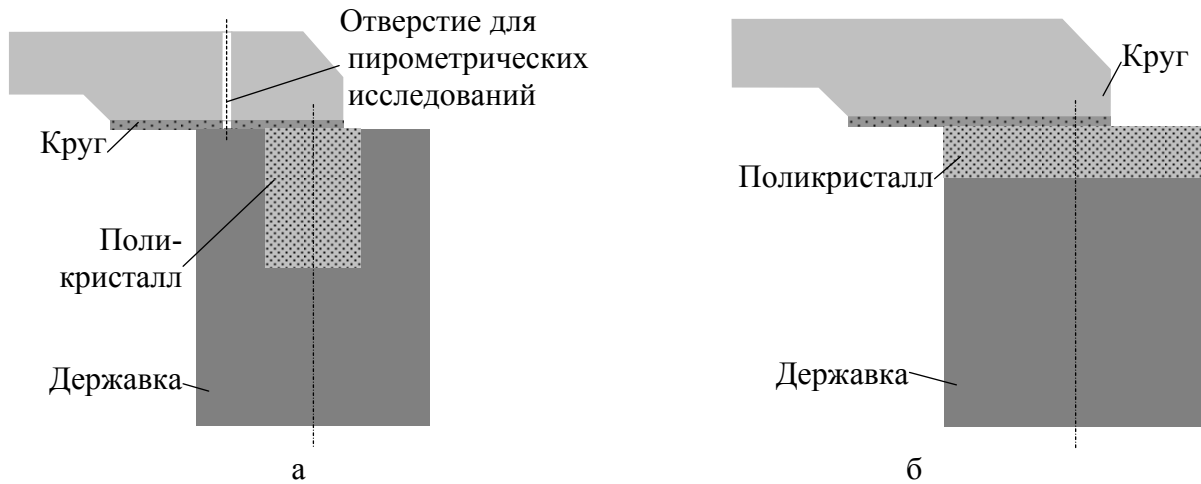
Торцевое шлифование сверхтвердого поликристалла в коаксиальной державке (а) и двухслойной заготовки со сверхтвердым поликристаллом (б)
